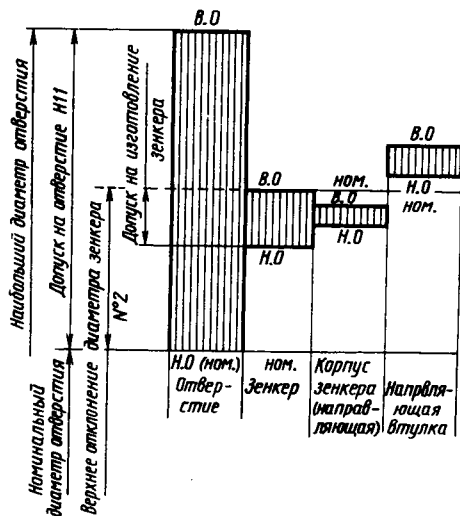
Схема построения допусков на наружный диаметр зенкера № 2:
